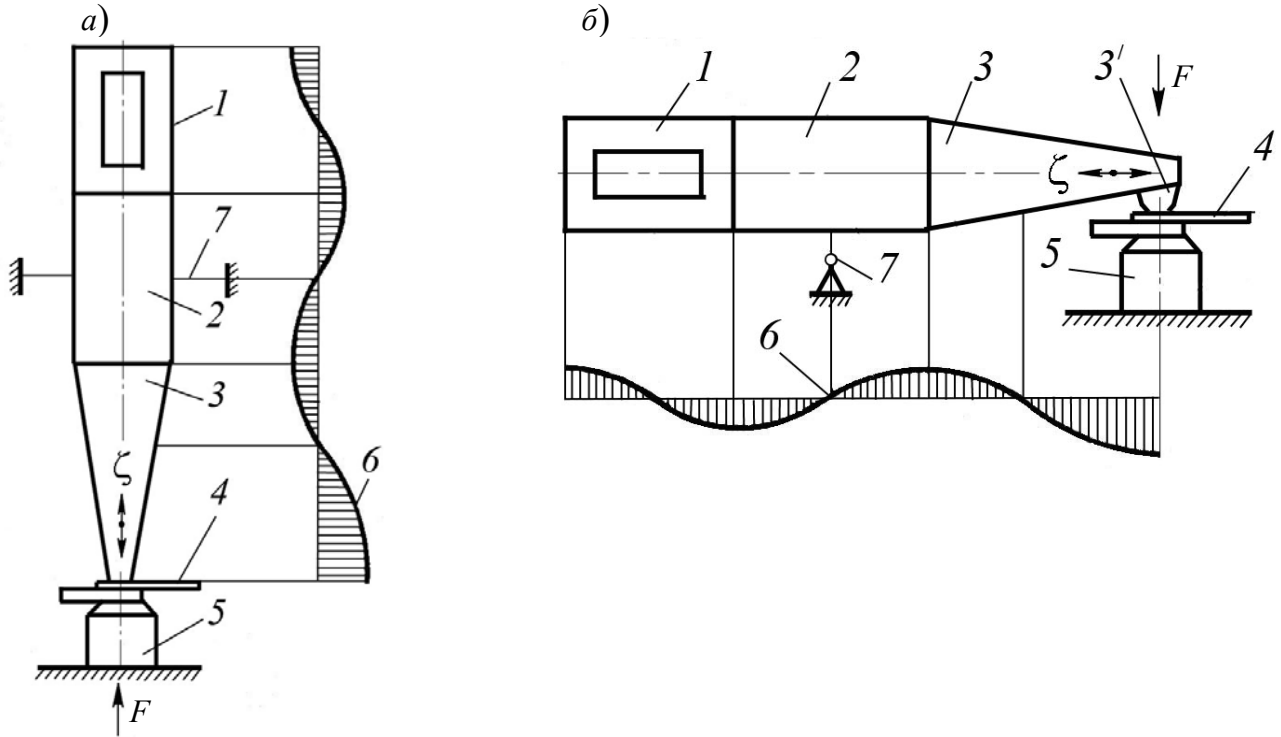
Классификация схем ультразвуковой сварки
